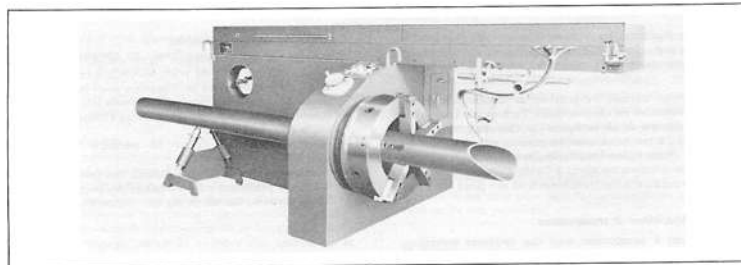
Machine pour la coupe des tubes et l'usinage des extrémités.
